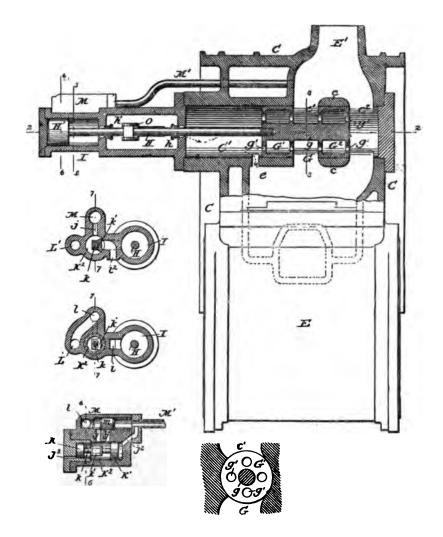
, 10, 11, 12. — Coupe du tiroir.
